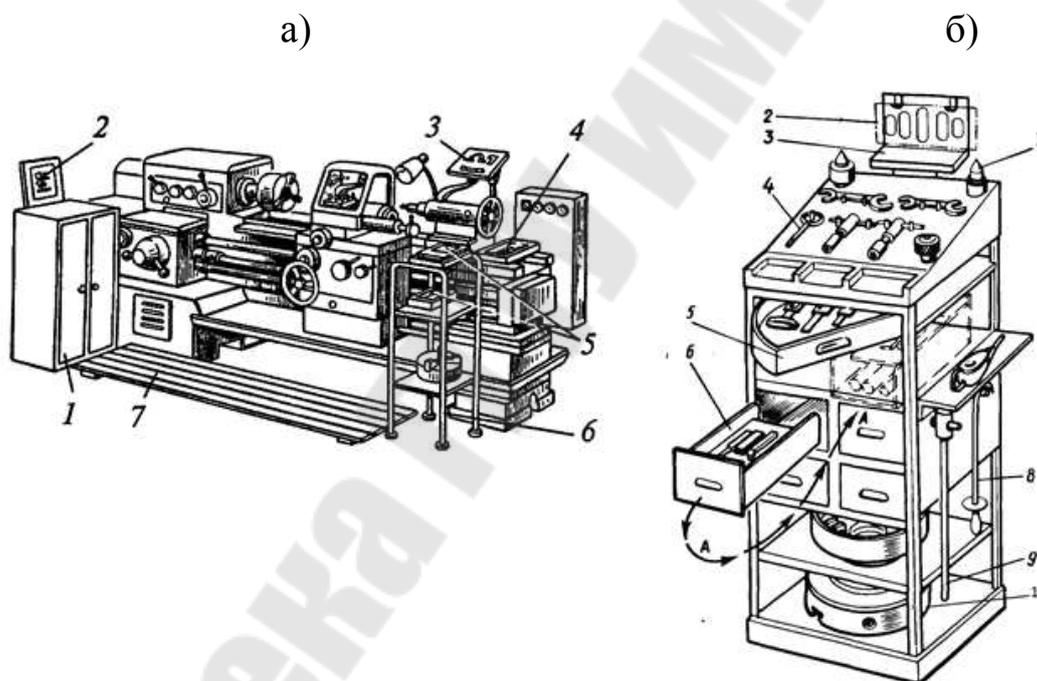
Планировка рабочего места токаря (а: 1 – инструментальный шкаф; 2 – планшет для чертежей; 3 – планшет для измерительных инструментов; 4 – ящик для вспомогательного инструмента; 5 – ящики для инструмента и деталей; 6 – стеллаж; 7 – решётка) и инструментальный ящик (б: 1 – патроны 2 – планшет; 3 полочка; 4 наклонная полочка с зажимным инструментом; 5 – поворотный ящик с измерительным инструментом; 6 – ящики с режущим инструментом; 7 – центра; 8 – скребок; 9 – пруток)
